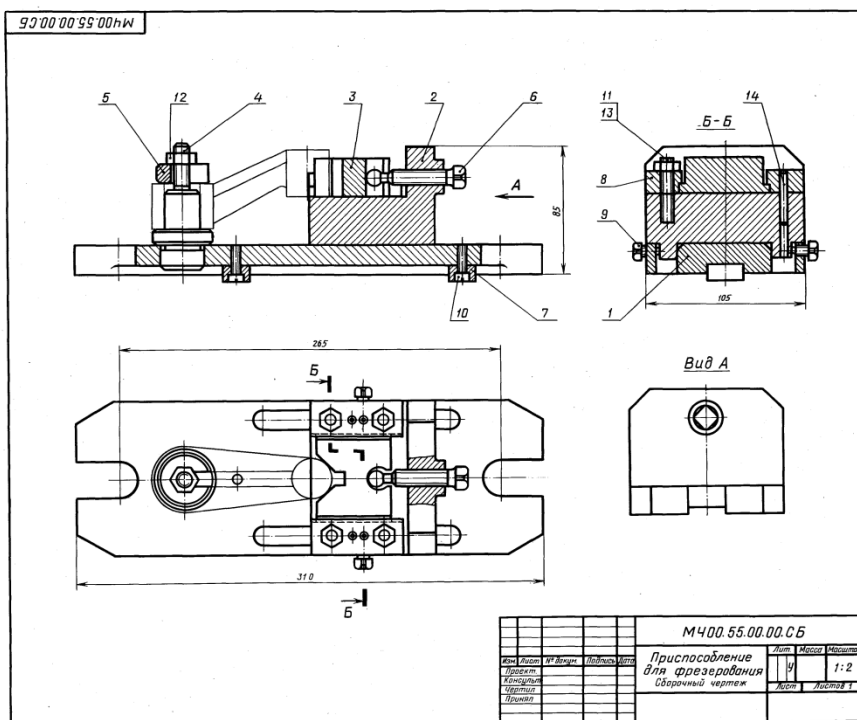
Сборочный чертёж «Приспособление для фрезерования»
